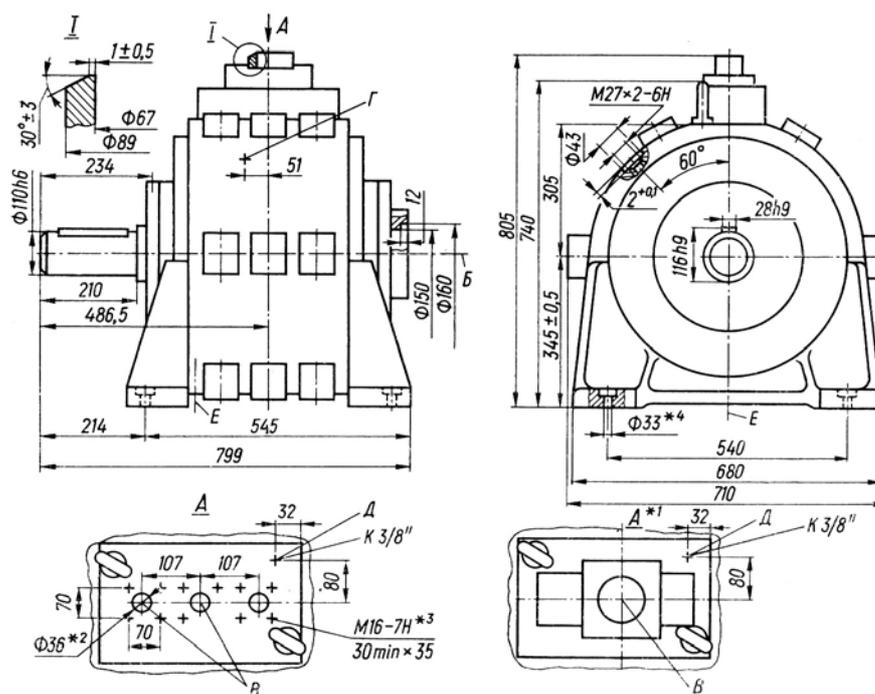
Основные габаритные и присоединительные размеры насосов типа НР2-1250/32 и НР2-900/32:
